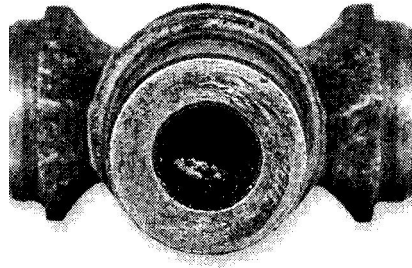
Сліди фретинг-корозії на торці цапфи хрестовини
